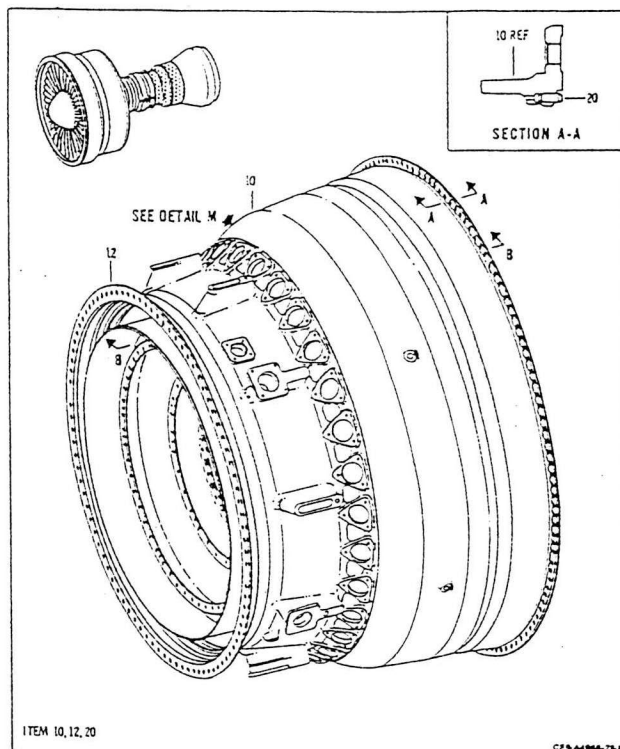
แสดงภาพ 2 B Module (High Pressure Compressor Rotor Assembly)
